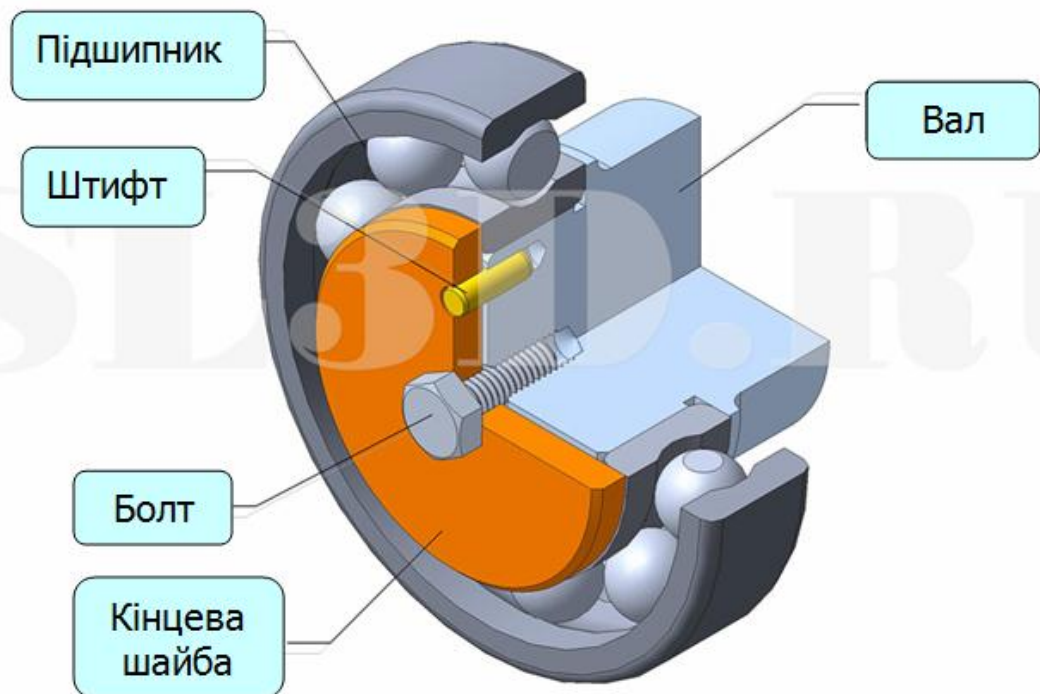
Установка підшипника з затягуванням кінцевою шайбою
